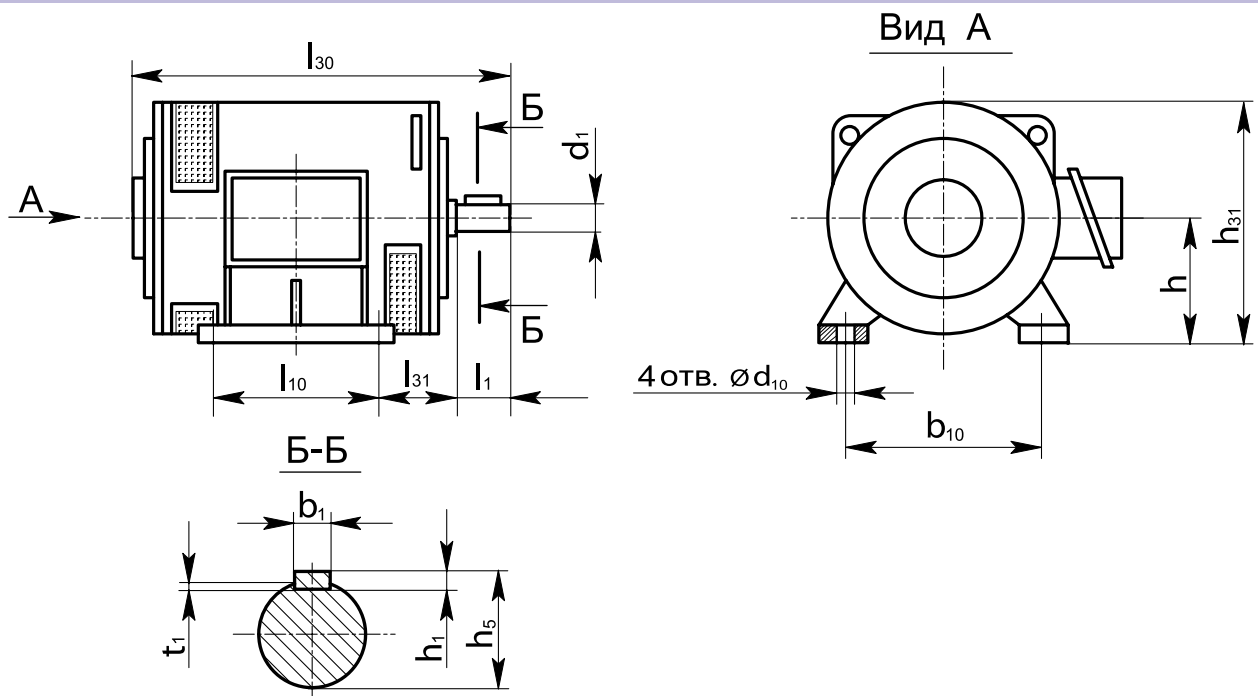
Габаритные, установочные и присоединительные размеры электрических машин типа ПМ81–ПМ82
